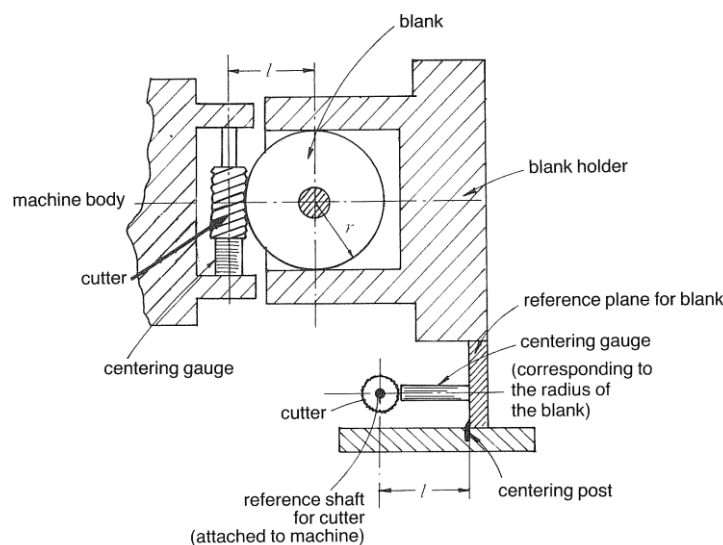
Regolare la posizione di un pezzo da lavorare
